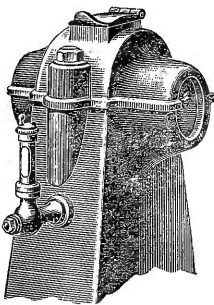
Vue d'ensemble d'un palier graisseur (Henrion).
